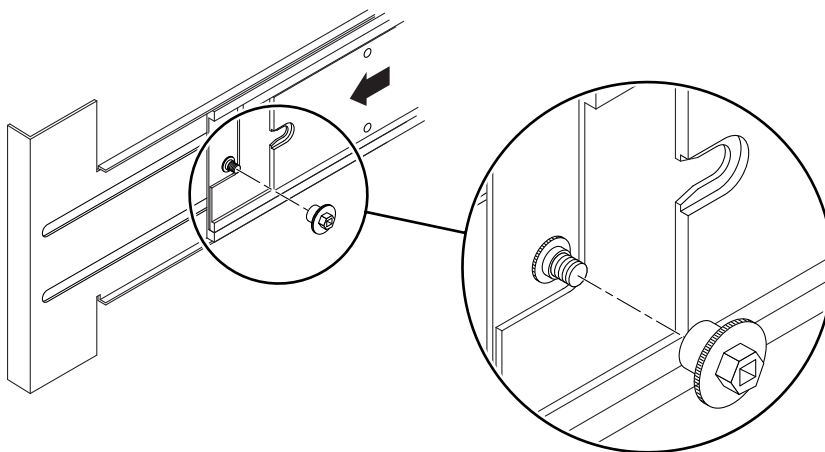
Inserimento e serraggio dei dadi di fissaggio delle guide
